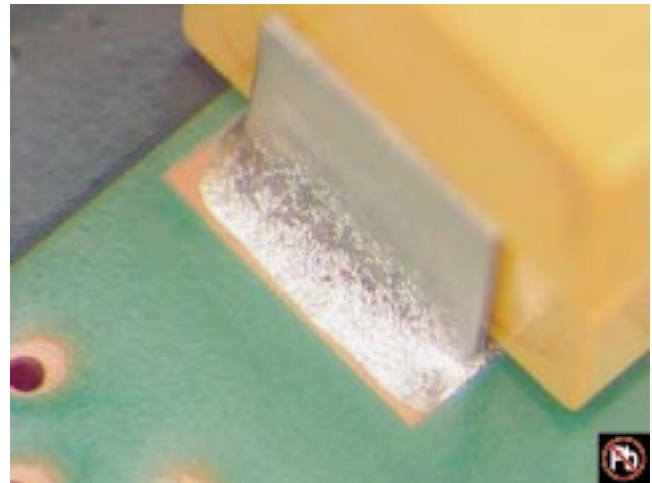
Soldadura SnAgCu; Flux Soluble en Agua
